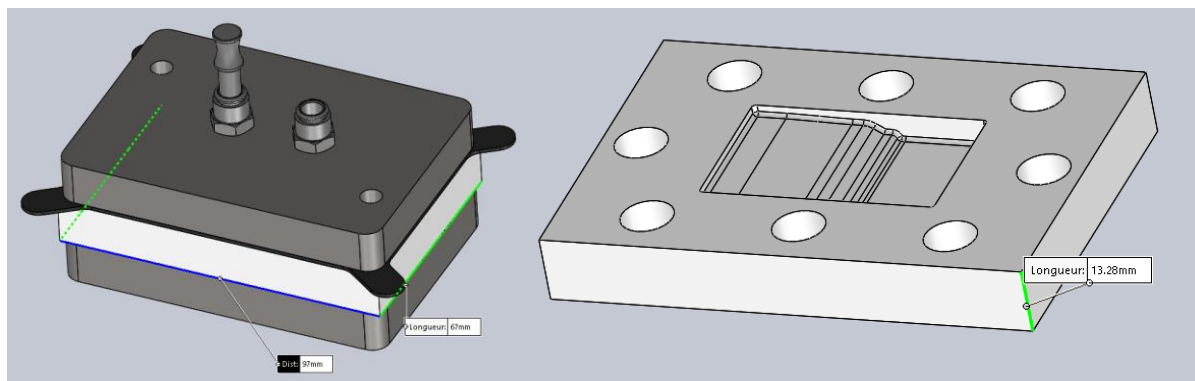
Vue d'ensemble du premier concept du moule et du filtre de cette version (les tranches devaient être scellées à la colle B7000, processus testé préalablement sur la matière poreuse). En blanc la pièce filtrante, en gris les pièces en aluminium et en noir le joint à languettes.
